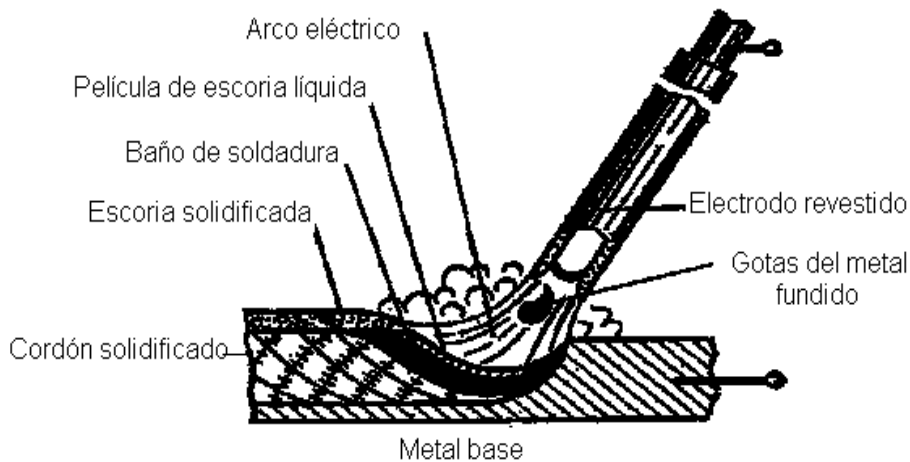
Esquema del proceso de soldeo SMAW. Fuente: Burgos (1989).
